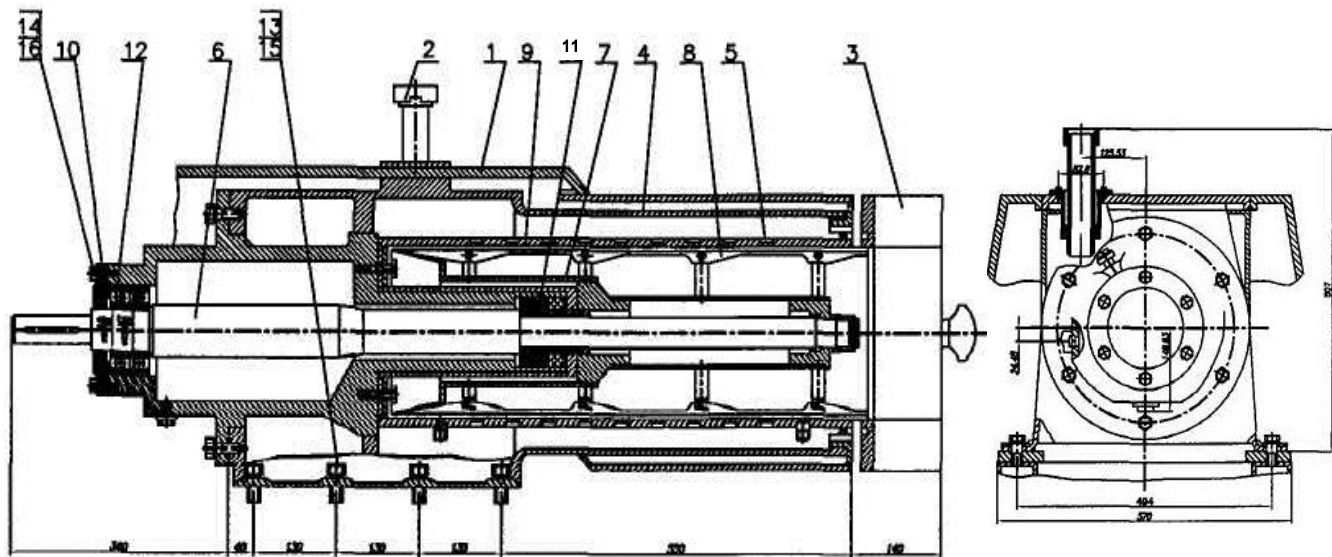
Збивач масловиготовлювача: 1 – корпус; 2 – штуцер подачі верхків; 3 – рукав; 4 – теплообмінна сорочка; 5 – сітчаста вставка; 6 – вал; 7 – корпус била; 8 – лопата; 9 – циліндр; 10 – кришка; 11, 12 – підшипники; 13, 14, 15, 16 – болтове кріплення
